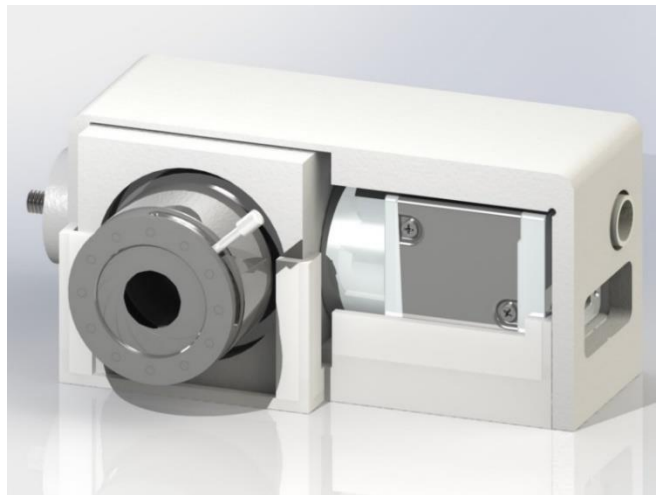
Imagem da geometria final do Interferómetro construído, vista pelo lado da lente de imagem.
